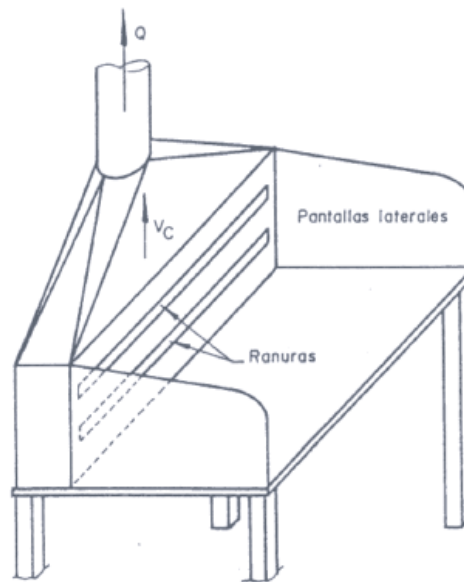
Ventilación para soldaduras. Soldadura sobre banco fijo.
